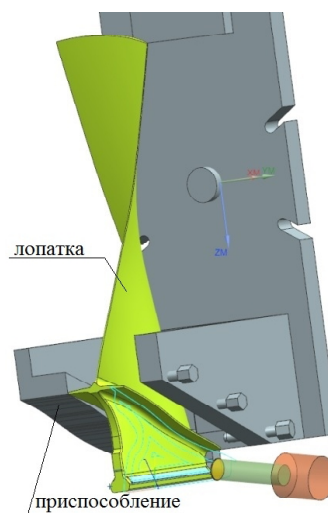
Обработка хвостовика лопадки на фрезерном станке с ЧПУ ИС-800
